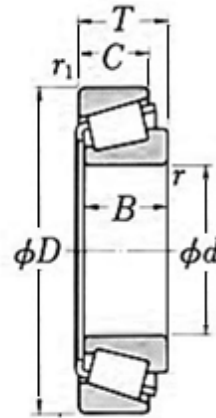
Rodamientos de rodillos cónicos (1 hilera)
